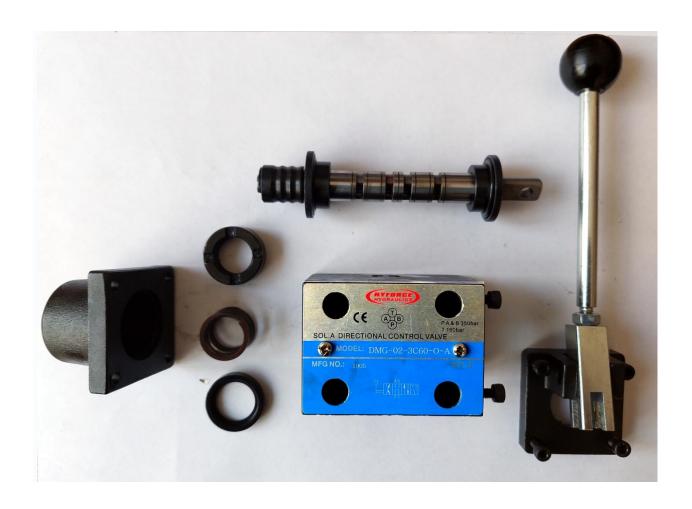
Трехпозиционный четырехлинейный распределитель DMG-02-3C60-O-A с ручным управлением в разобранном виде
